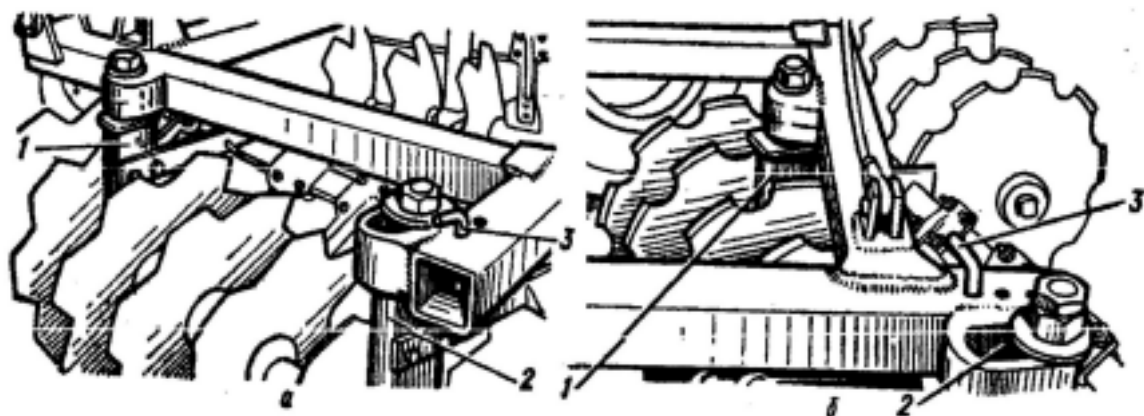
Пристрій для регулювання кута атаки батарей дискової борони БДВ-7:
